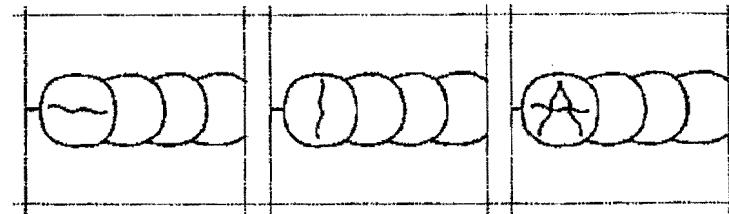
28. Кратерная трещина сварного соединения
